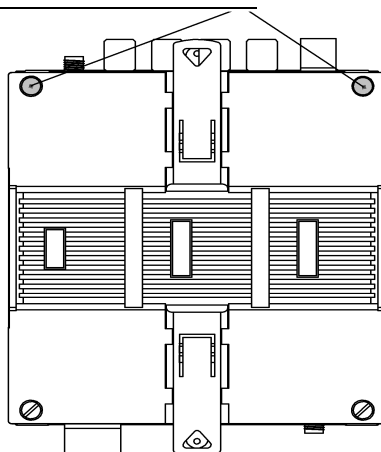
Место нанесения знака поверки на ББ (вид сзади)
